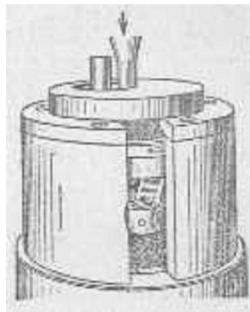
Выпрессовка среднего опорного пальца из маховика
